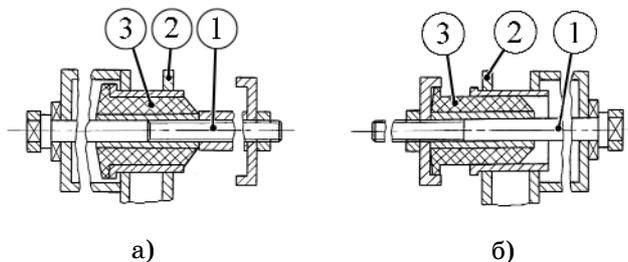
Схема выпрессовки (запрессовки) шарнира рычага задней подвески:
